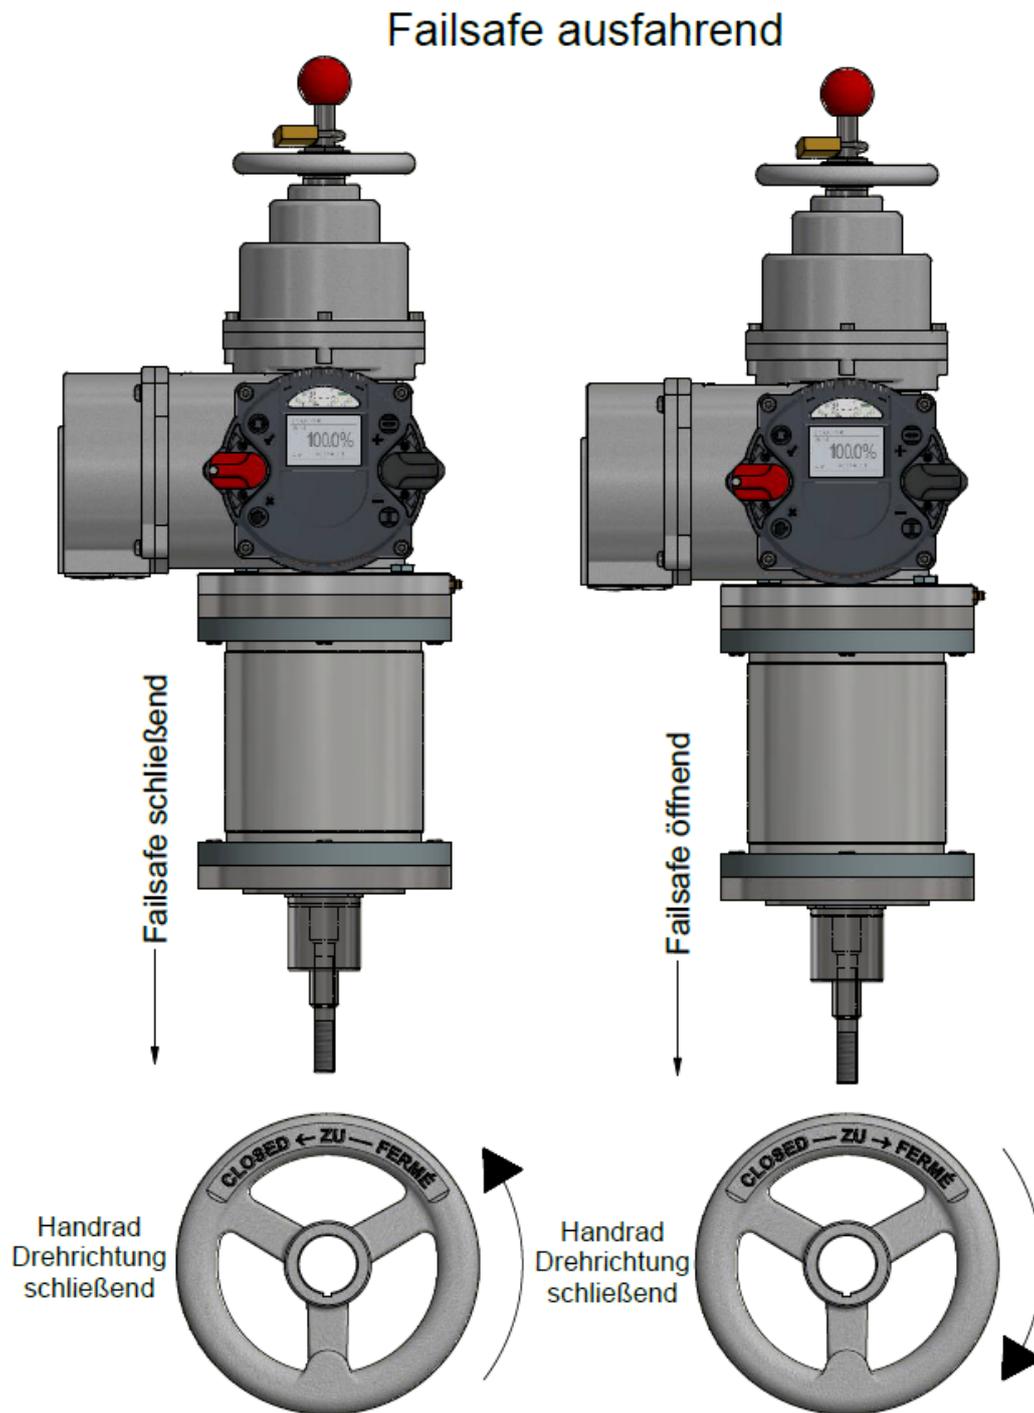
Drehrichtung des Handrades für Failsafe „ausfahrend“.
